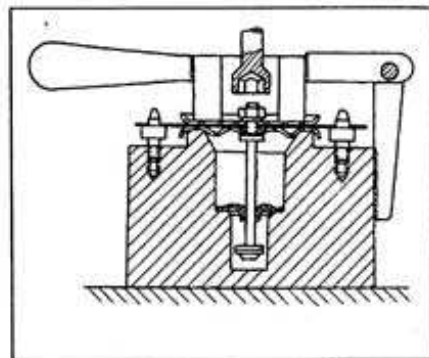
Приспособление для сборки диафрагмы топливного насоса
